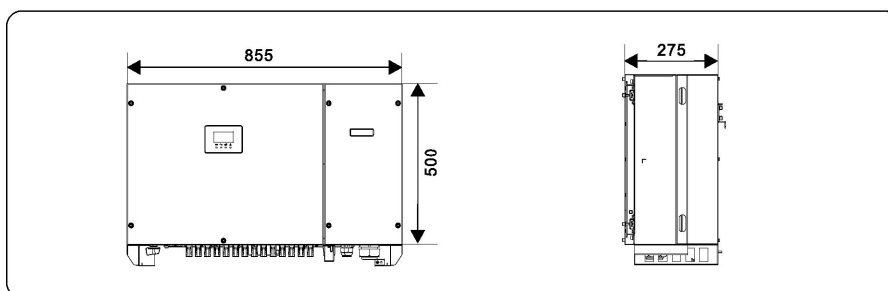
Dimensiones del inversor (unidades: mm)
